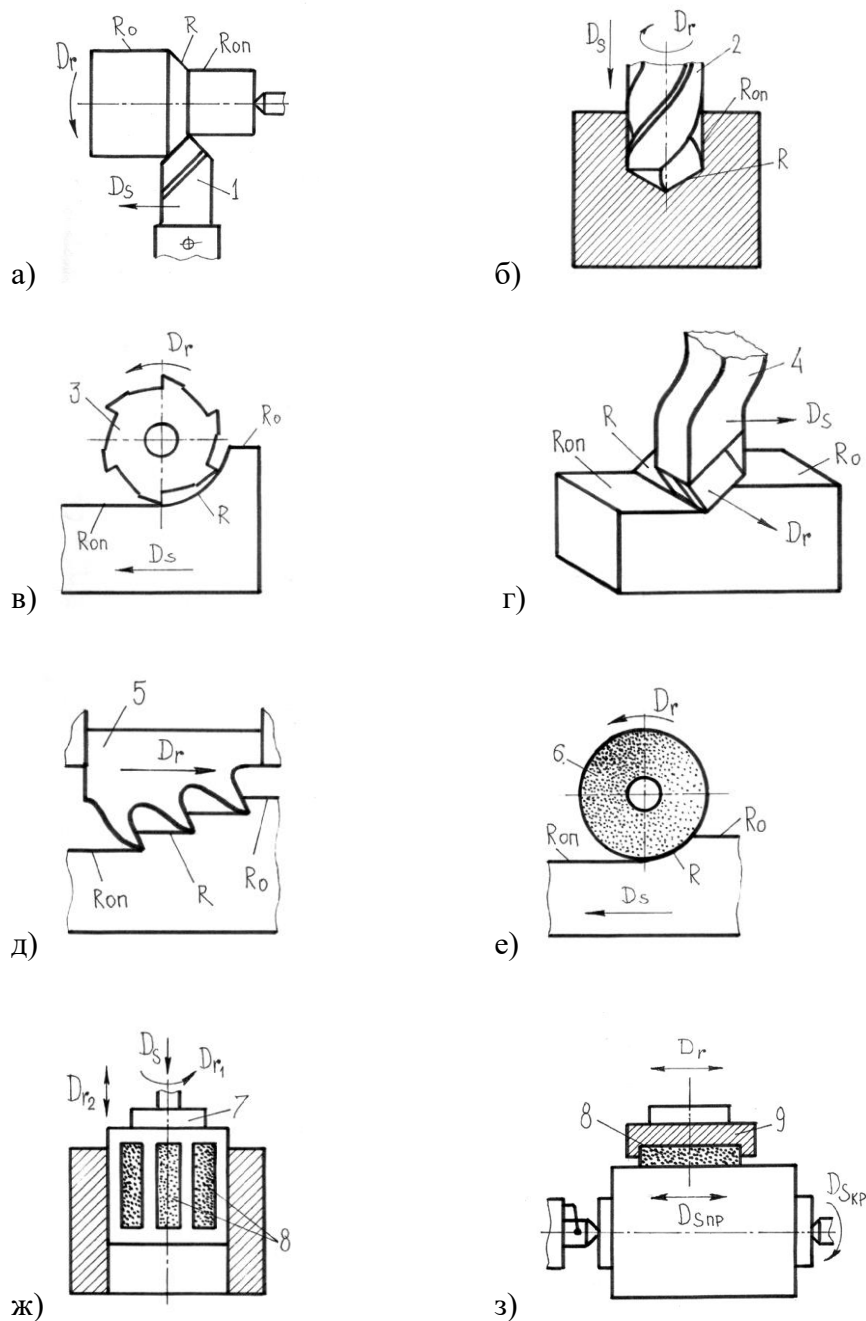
Схемы способов обработки резанием: *a* — точение; *б* — сверление; *в* — фрезерование; *г* — строгание; *д* — протягивание; *е* — шлифование; *ж* — хонингование; *з* — суперфиниширование
